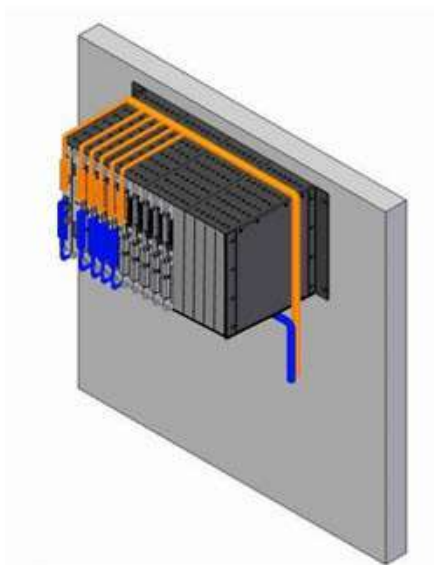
Монтаж на стенку, без крышки, без дисплея
